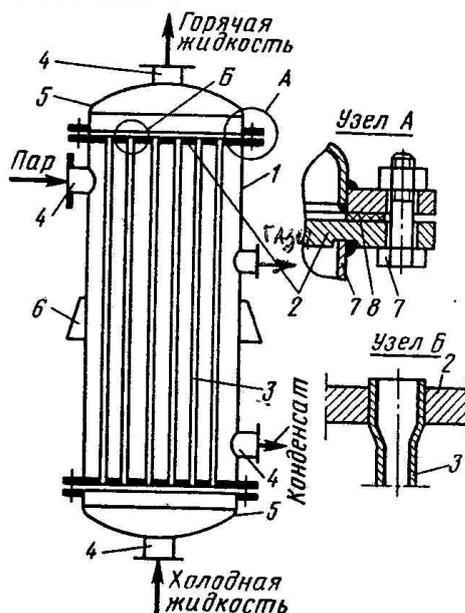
Схема вертикального одноходового кожухотрубчатого теплообменника с неподвижными трубчатыми решетками (а) и размещение труб в трубчатой решетке (б):
